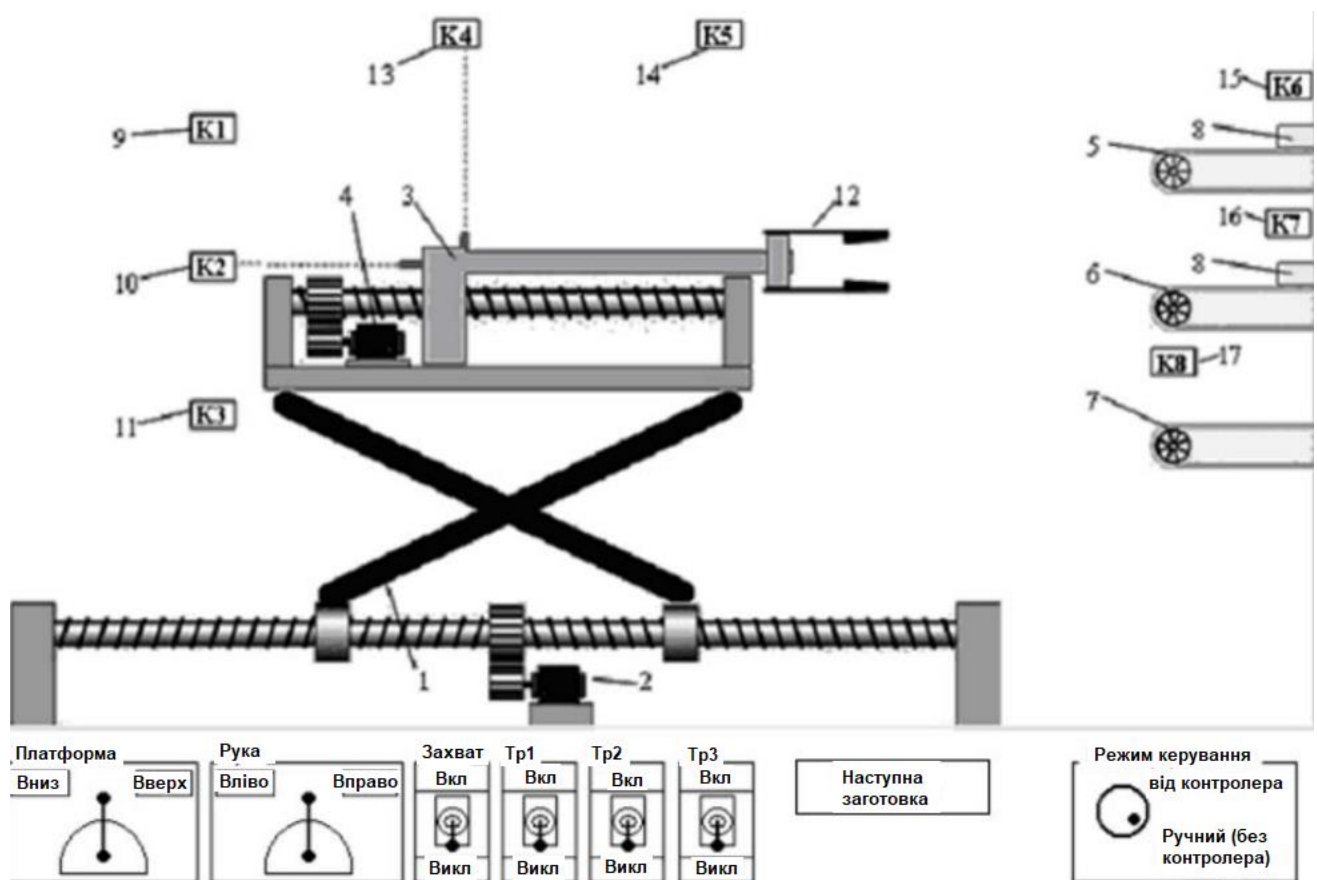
Загальний вигляд РК переміщення заготовок
